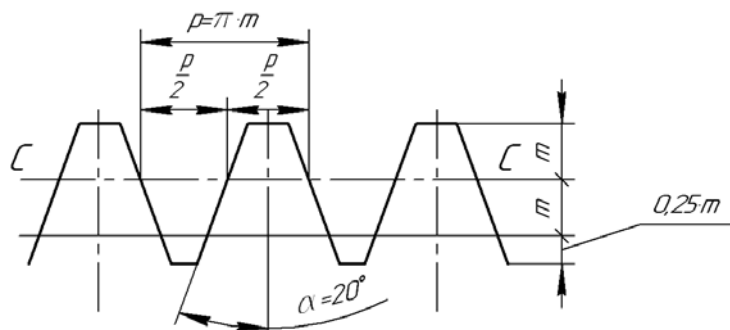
Основные параметры профиля зуба зубчатой рейки
